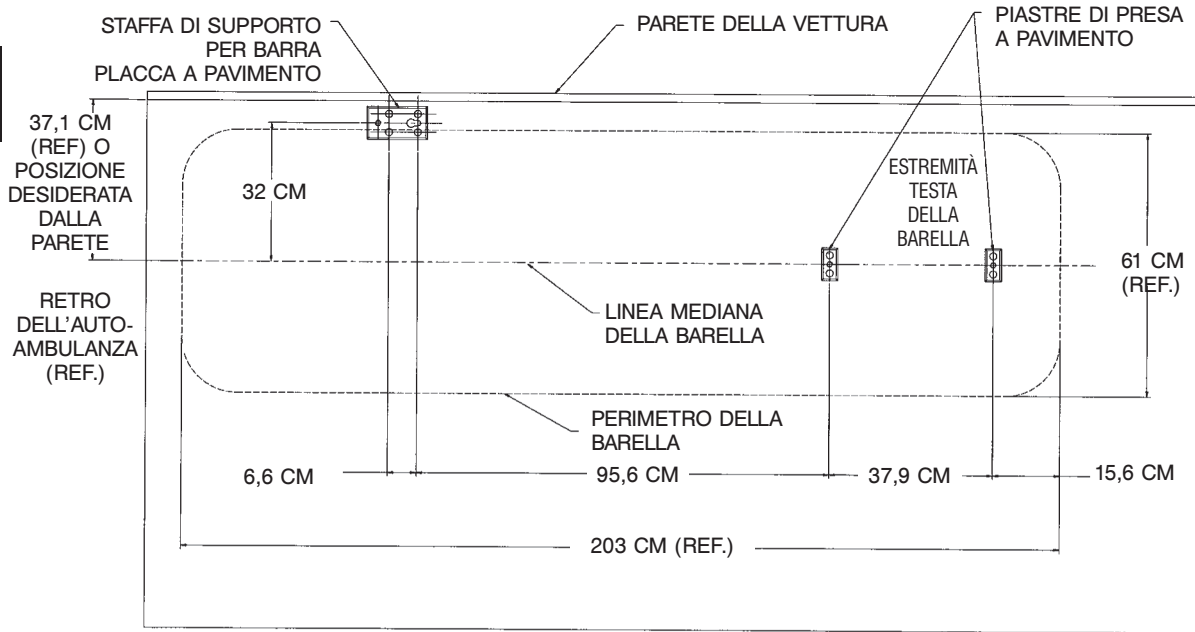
Dati tecnici di installazione - Sistema di ancoraggio a pavimento
